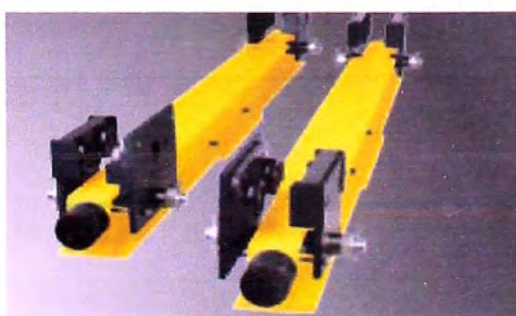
Vigas Testera Apoyadas y Suspendidas
